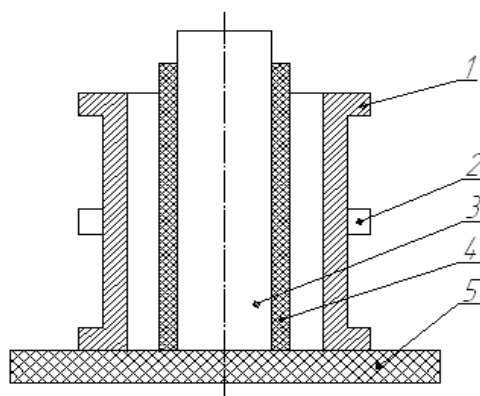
Схема сборки корпуса подшипника для заливки баббита
